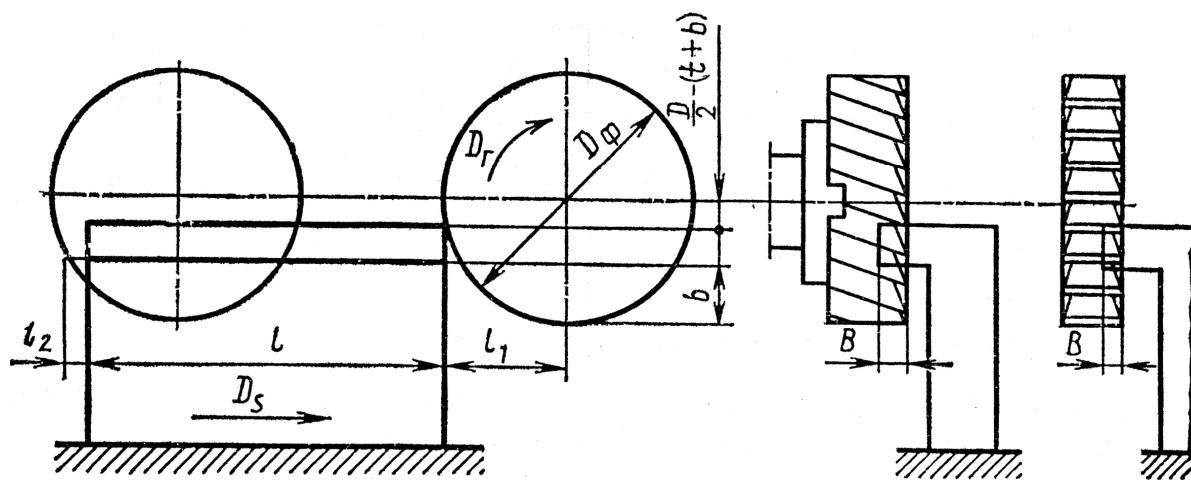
Путь, пройденный инструментом при несимметричном фрезеровании торцевыми и дисковыми фрезами
